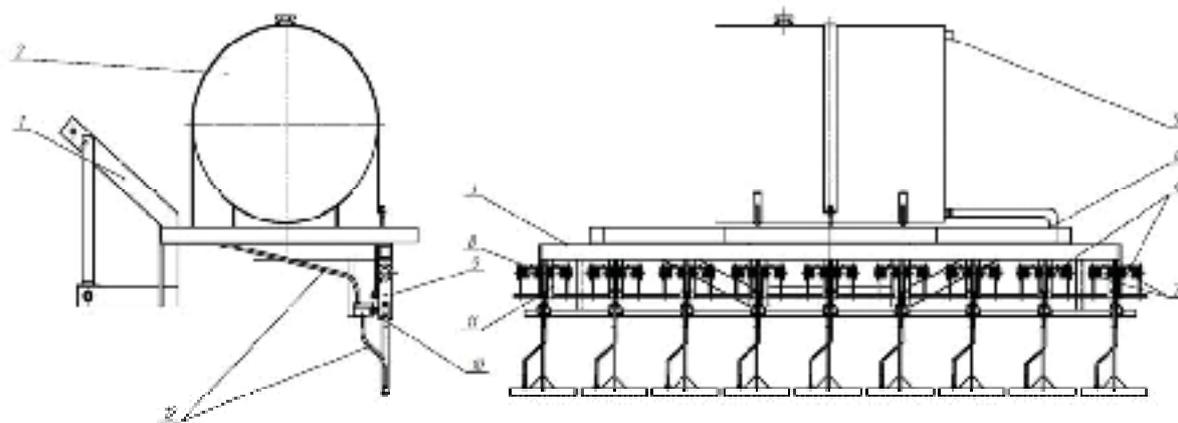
Устройство для подавления пней: 1 – рама навески; 2 – емкость с арборицидом; 3 – рама устройства для подавления пней; 4 – коллектор; 5 – предохранительный клапан; 6 – ось; 7 – пружина; 8 – шайба; 9 – рабочий орган; 10 – клапан; 11 – стопор; 12 – гибкие трубопроводы
